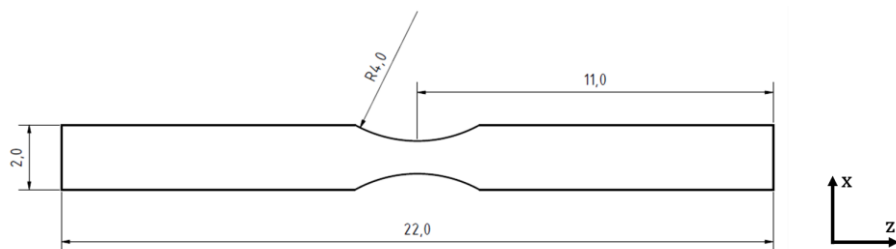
Probengeometrie der beidseitig gekerbten Aluminium-Zugprobe.
